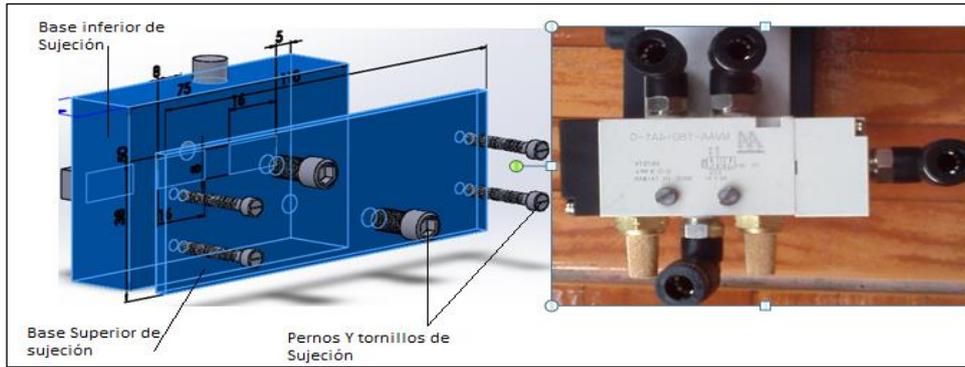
Elementos de fijación y válvula neumática retorno por muelle.
